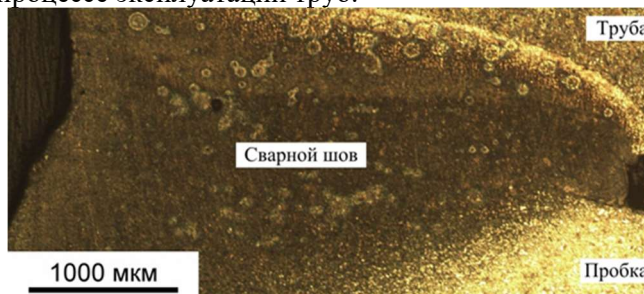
Макроструктура сварного соединения [14].
